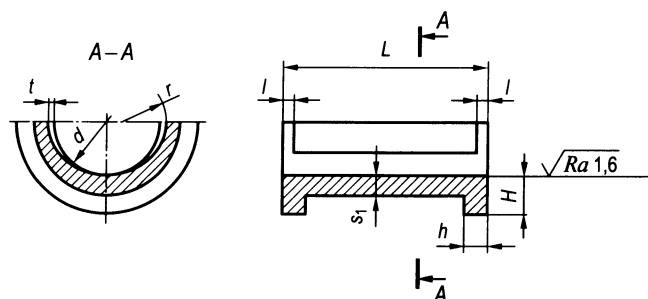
Конструкция и размеры вкладыша подшипника
